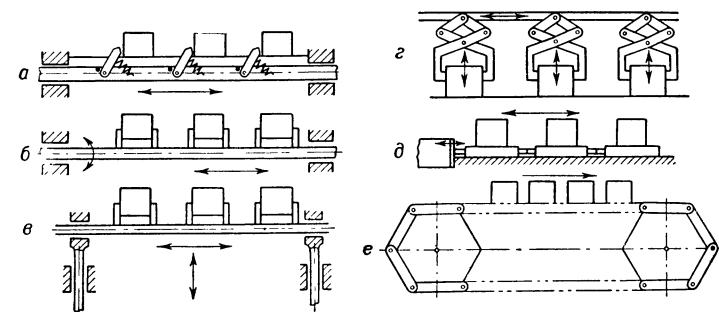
Схемы шаговых транспортеров автоматич. линий: а — с собачками; б — с фланжками; в — грейферный; г — рейнерный; д — толкающий; е — цепной.
